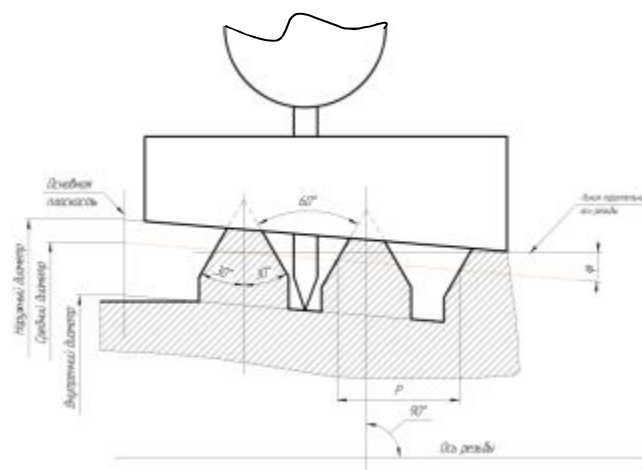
Измерение высоты замковой резьбы на трубе
